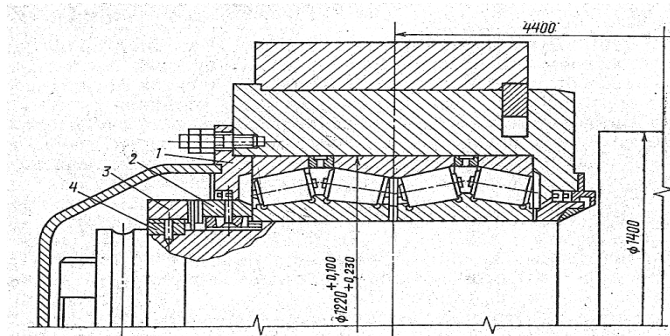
Установка опорного валка на роликовых конических подшипниках
